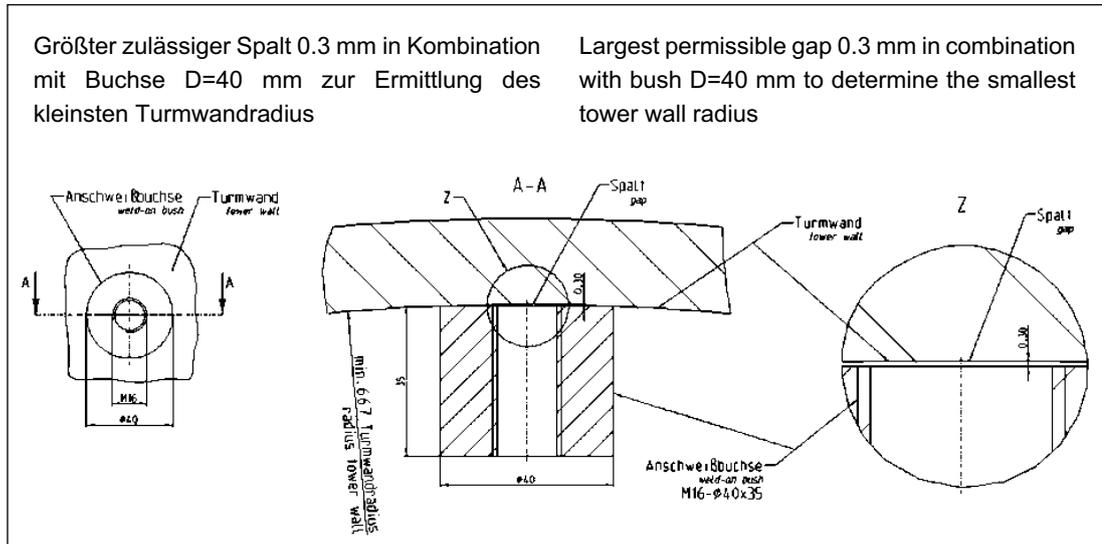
Detail Standard-Anschweißbuchse auf gekrümmten Mantelblechen
